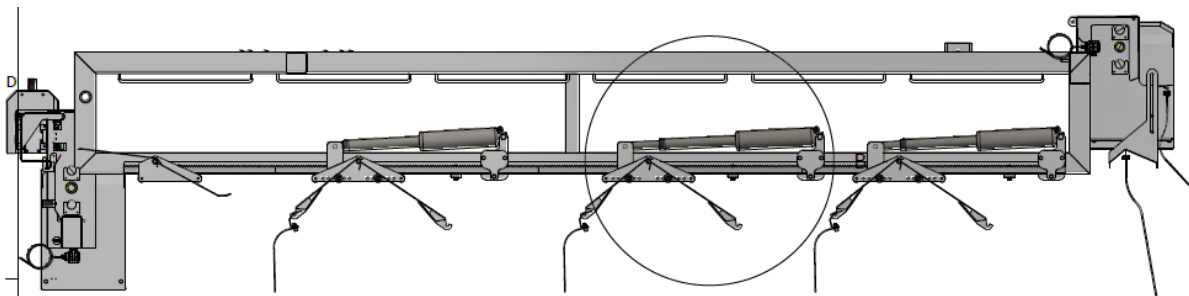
Bilde fra anlegg og pilotinstallasjon.
